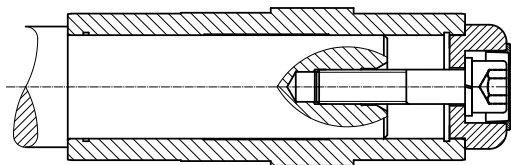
riduttore fissato ad un albero con spallamento mediante elemento di fissaggio
